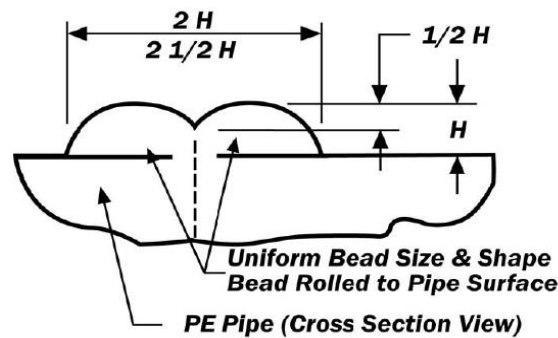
Illustration schématique pour soudage bout à bout [71].
